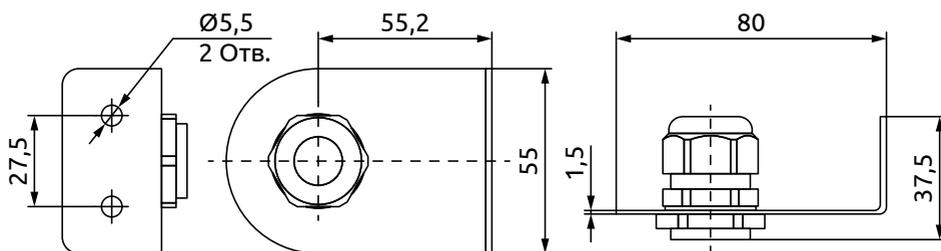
Габаритные размеры консоли HTE-HoldW
